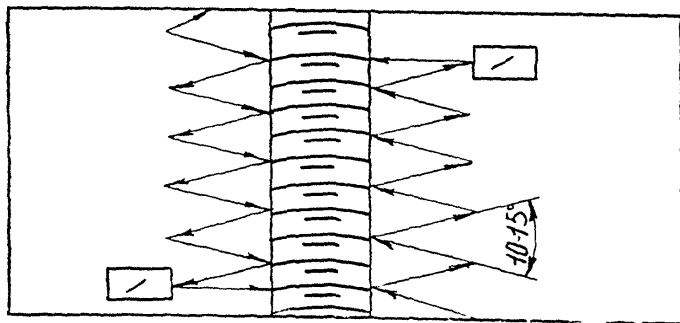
Схема перемещения искателя по поверхности при контроле сварного шва
